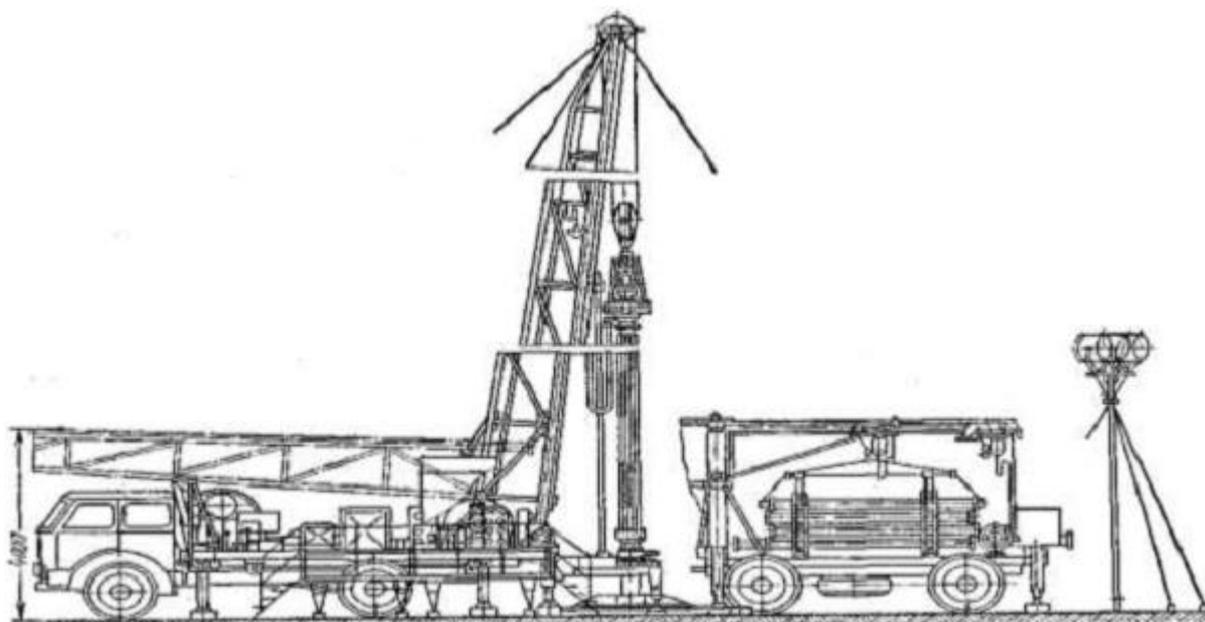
Буровой агрегат БА15.06 вид с боку
